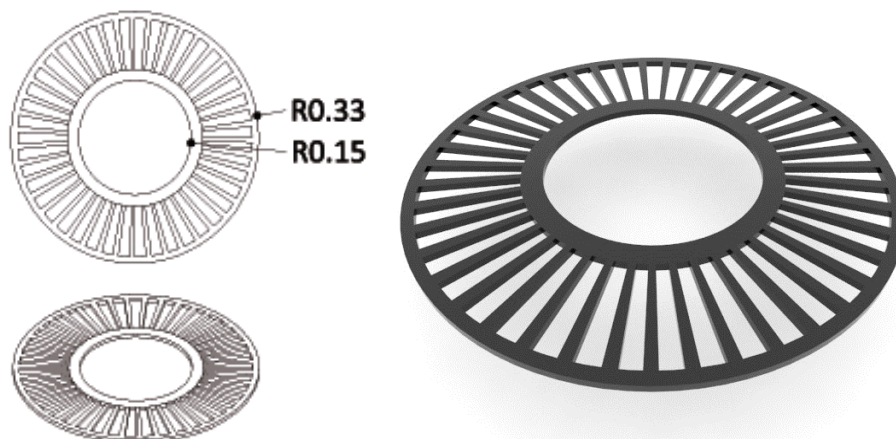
Planimetría y render, rejilla metálica 2. Fuente: grupo de investigación.
